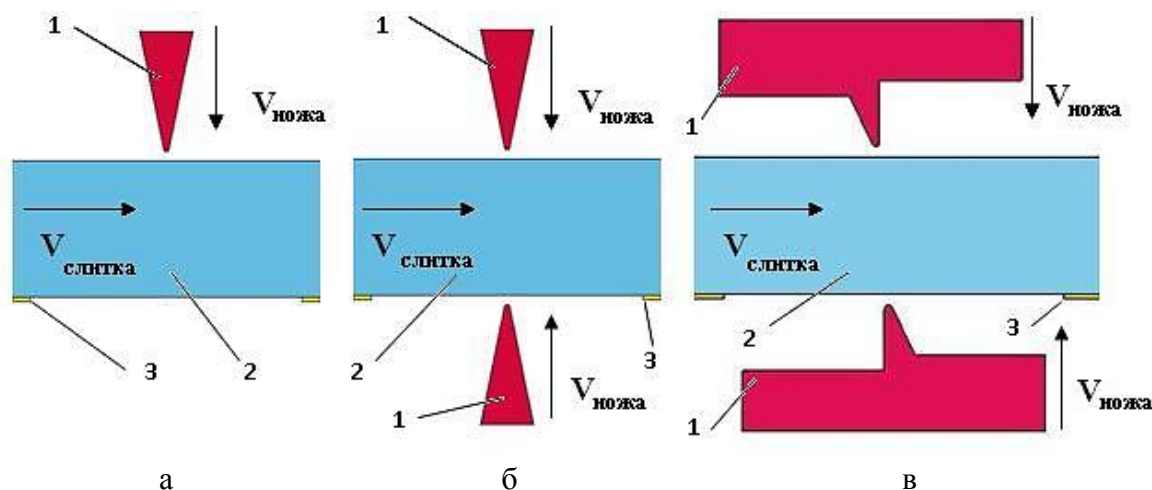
Объекты технологической зоны (1 – нож; 2 – слиток; 3 – опорные поверхности). Схемы реза (а – рез напроход одним ножом; б – рез двумя симметричными ножами; в – полусрезная схема клиновидными ножами
